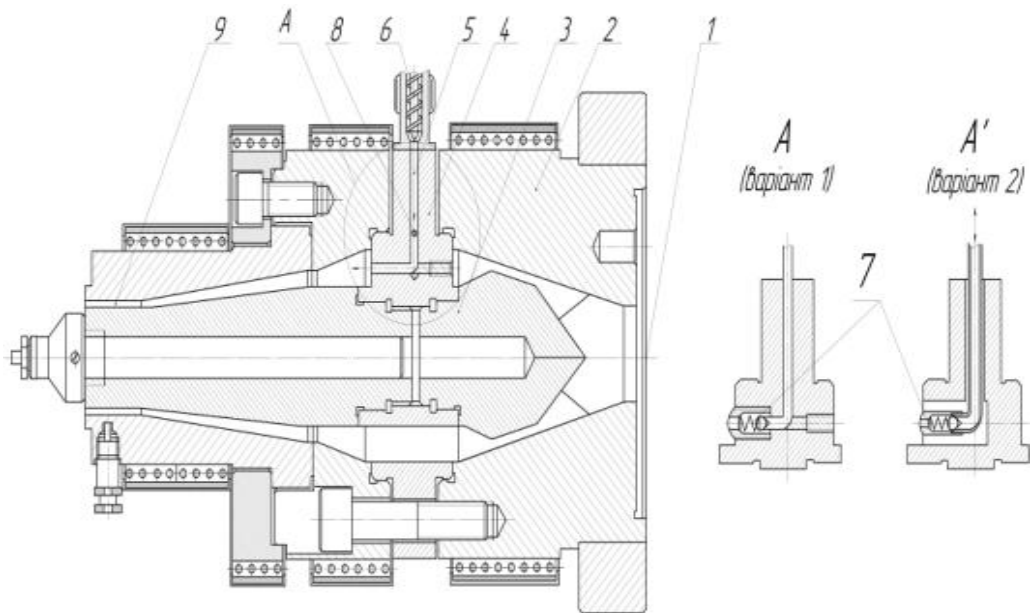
1 - Кільцева екструзійна головка для виготовлення труб
